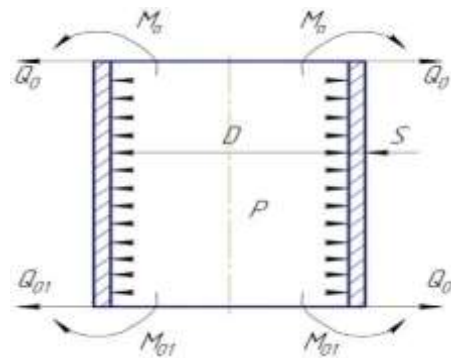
Розрахункова схема циліндричної обичайки
